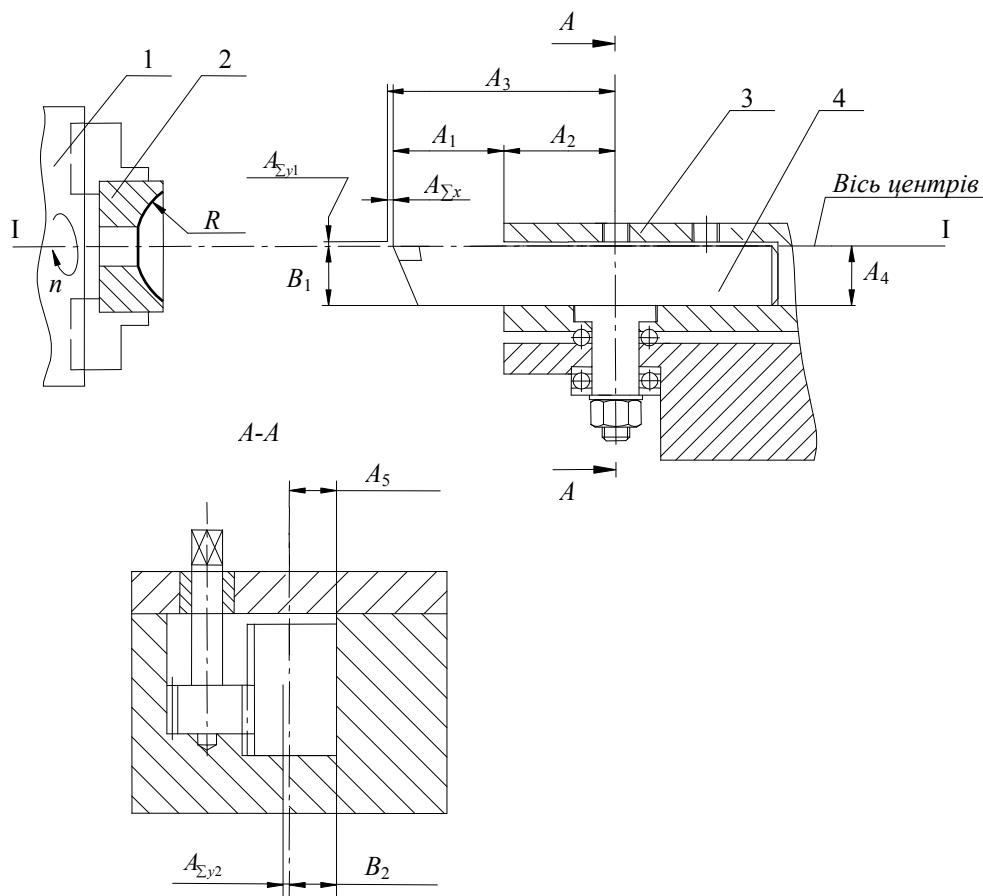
Розрахункова схема точності оброблення сферичної поверхні
